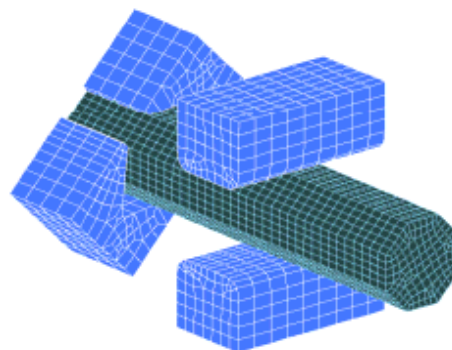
Конечно элементная модель процесса протяжки заготовки из сплава Inconel 718
